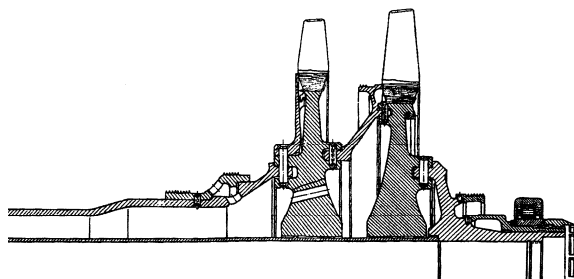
Ротор ТВД с «вилчатым» штифтовым соединением [9].
